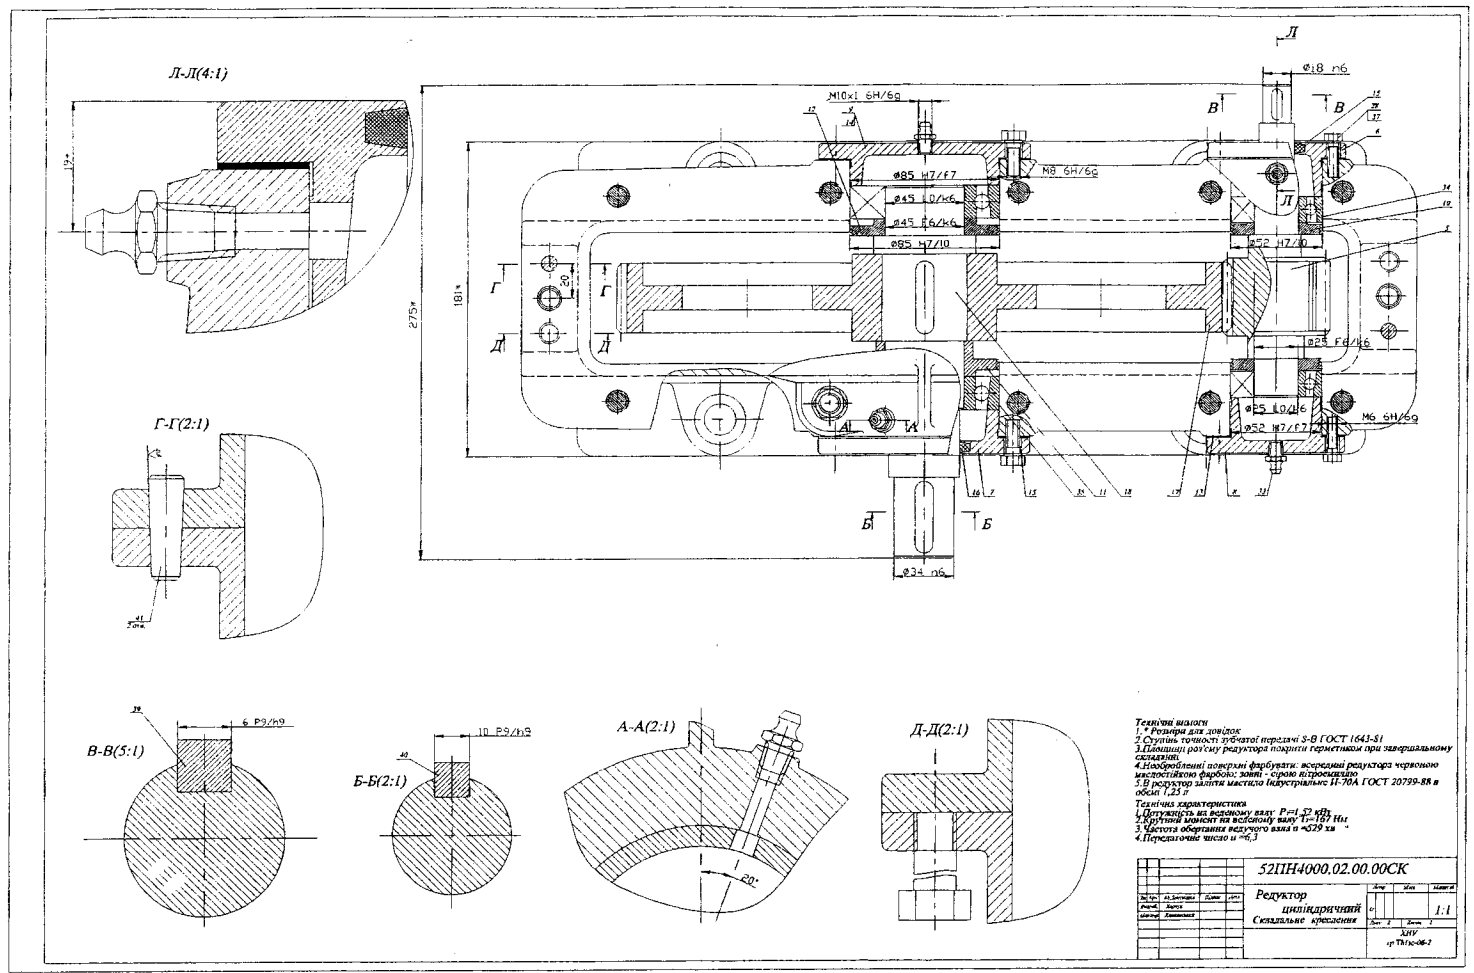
Циліндричний редуктор (аркуш 1)
